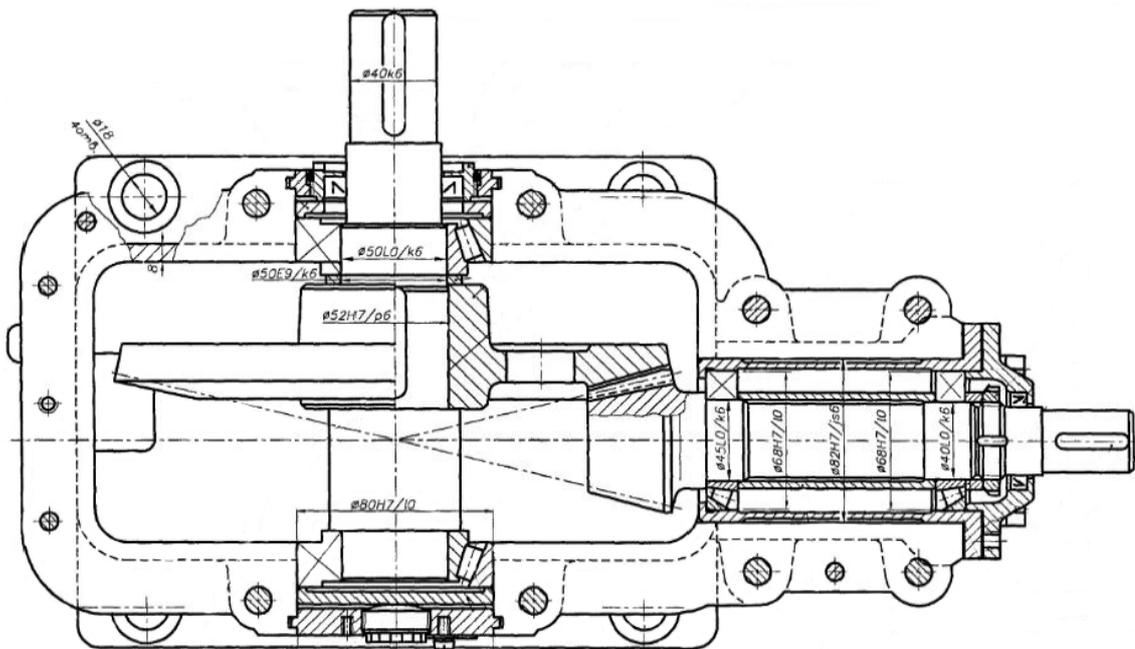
Конический редуктор [4]. Быстроходный вал установлен в распор.
